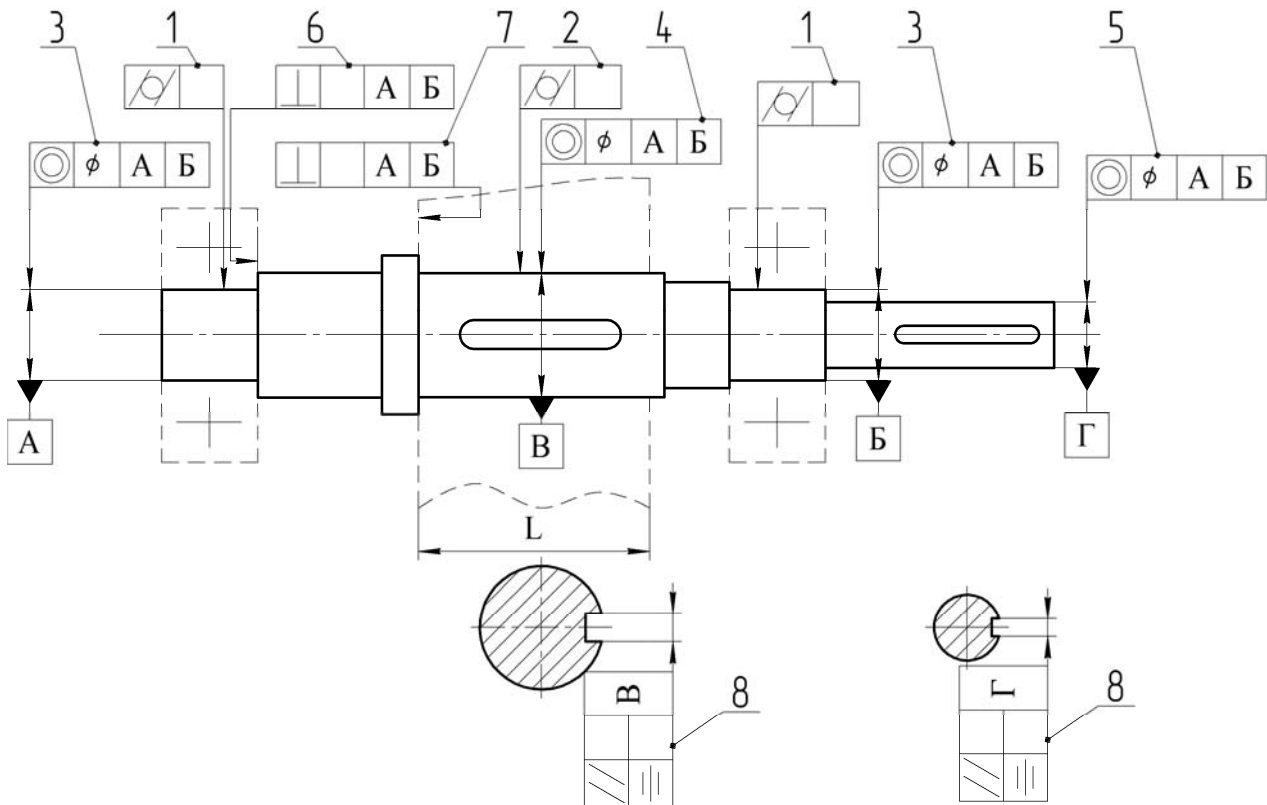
Допуски формы и расположения поверхностей вала
